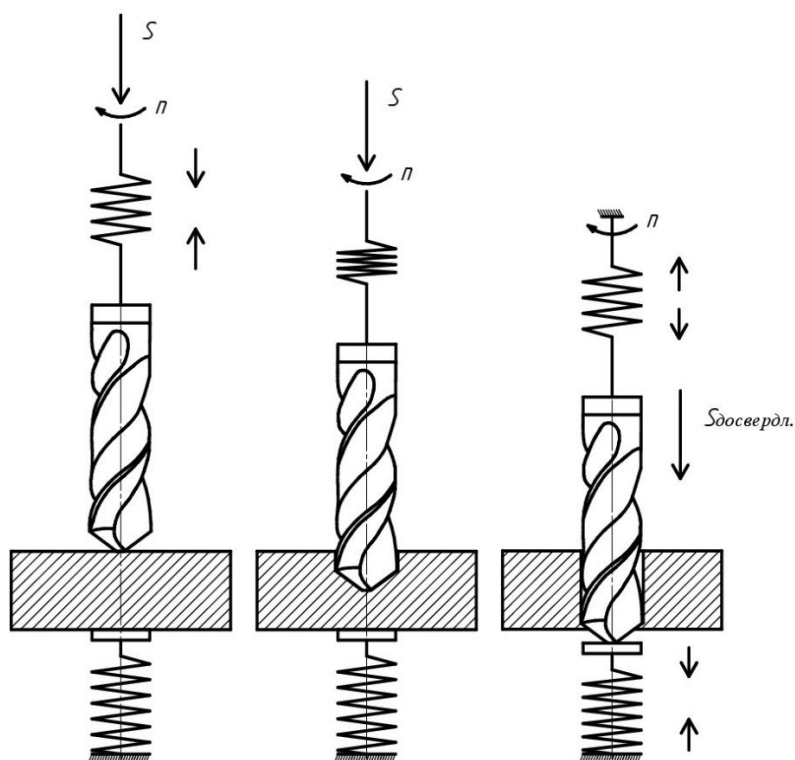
Схема роботи пристрою для свердління наскрізного отвору з підпорною п'яткою
